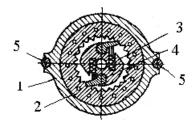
Поворотный механизм с двумя собачками в корпусе: 1 — букса; 2 — храповое кольцо; 3 — пружина; 4 — храповой стержень; 5 — болт.
